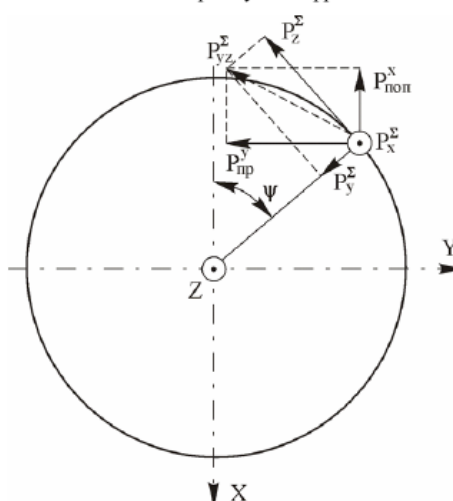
Разложение сил, действующих на зуб концевой радиусной фрезы, в системе координат станка
